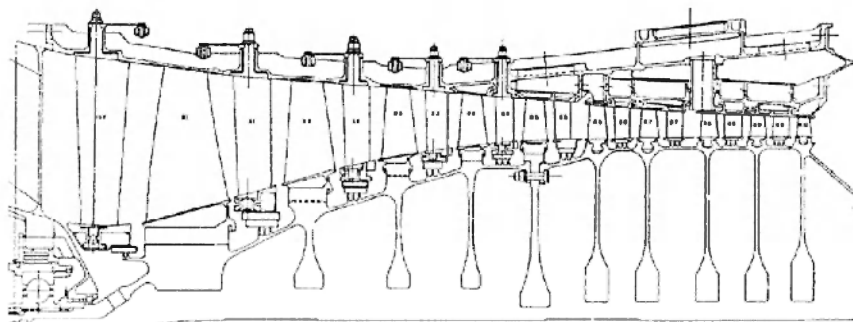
Компрессор высокого давления двигателя E3-GE
